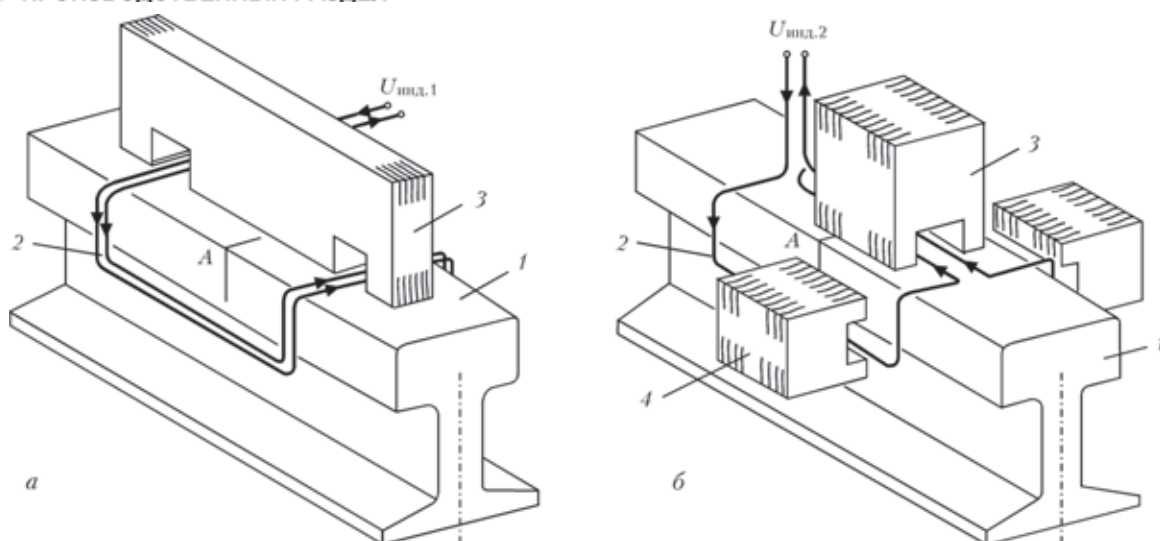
Конструкции индукторов 1 (а) и 2 (б) для нагрева головки рельса: 1 — рельс типа Р65; 2 — индуктирующий провод; 3 — основной магнитопровод; 4 — дополнительные магнитопроводы
